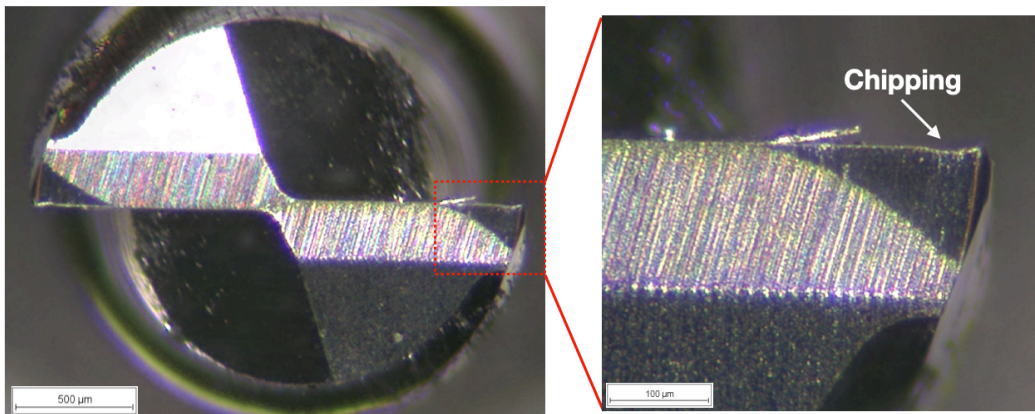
進給率 800 mm/min 之刀具 chipping 現象
